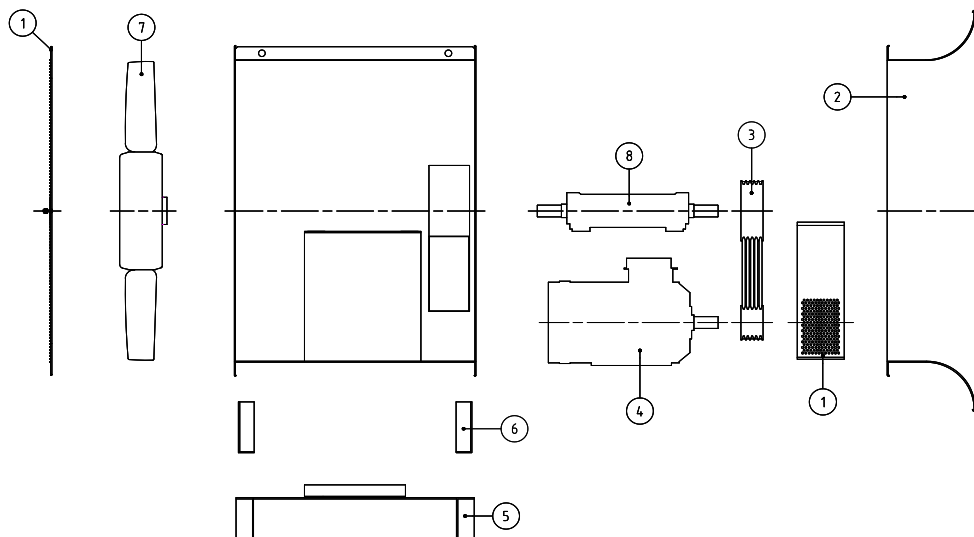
Explosionszeichnung des Ventilators in Ausführung 12
